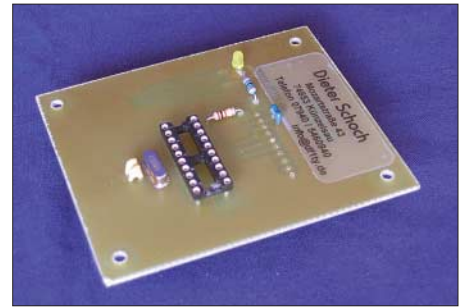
Auf das Basisboard lässt sich z. B. dieser Adapter für 20-polige AVR aufstecken.
